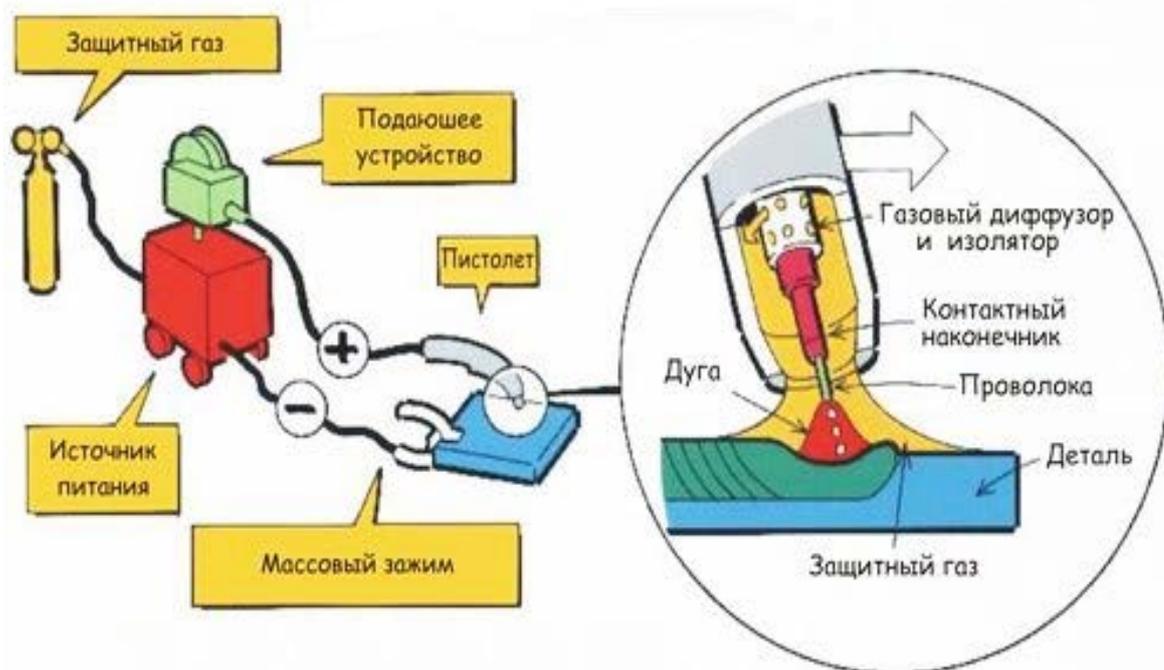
Полуавтоматическая сварка для сборки ребер
